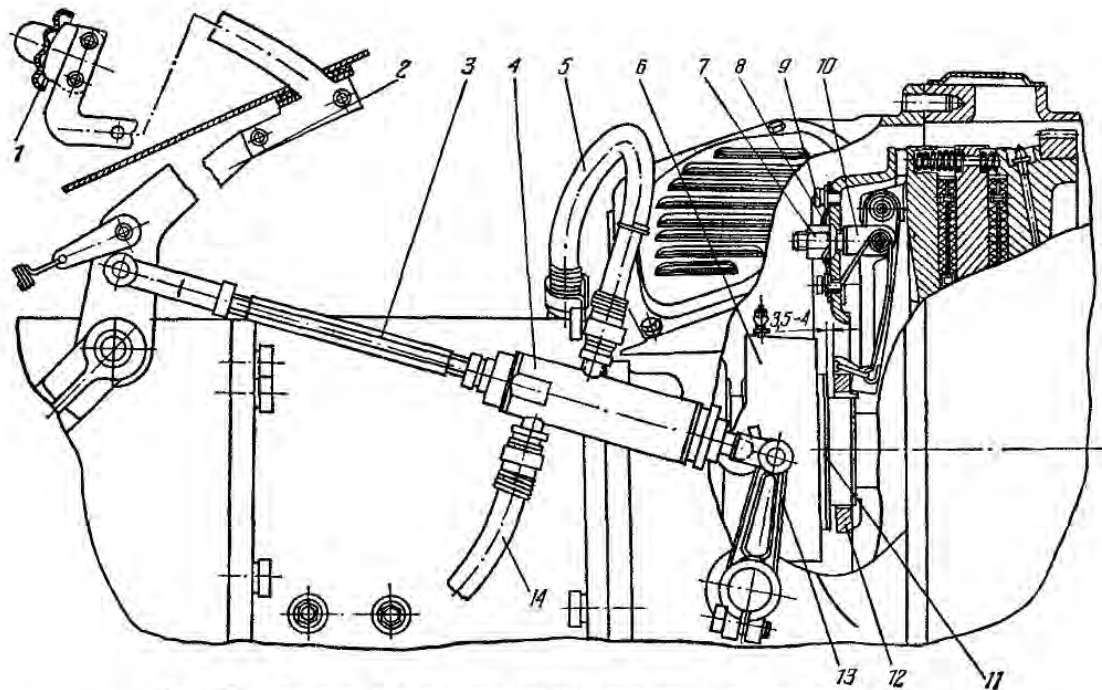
Привод выключения муфты сцепления трактора Т-150К:
